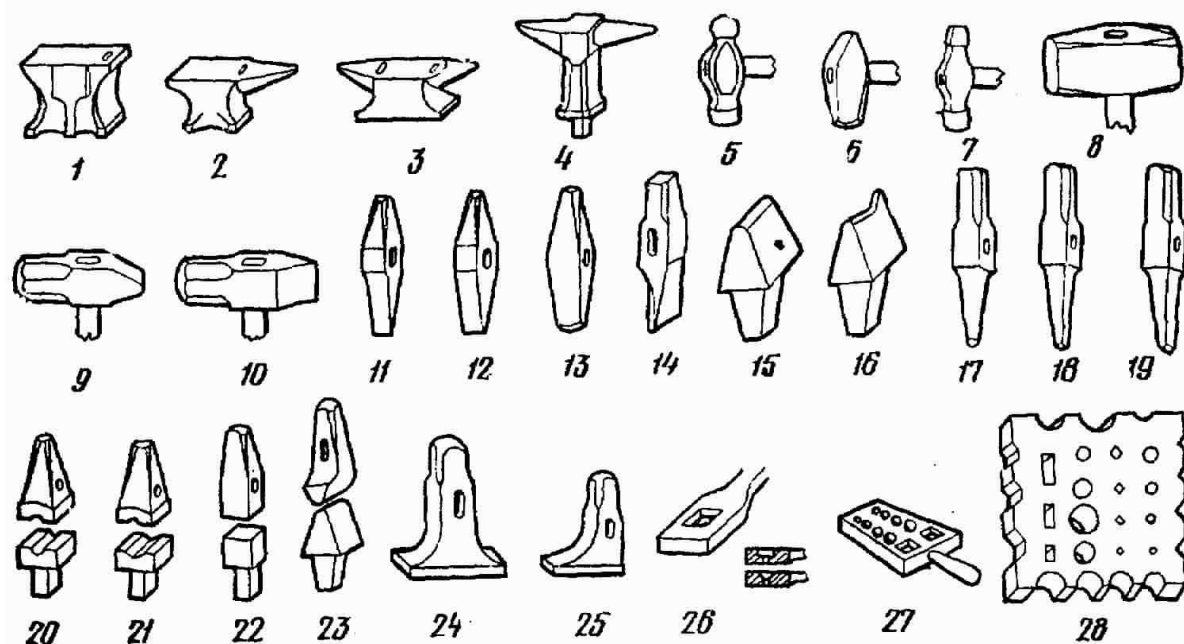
Схематическое исполнение инструмента для ручнойковки:
